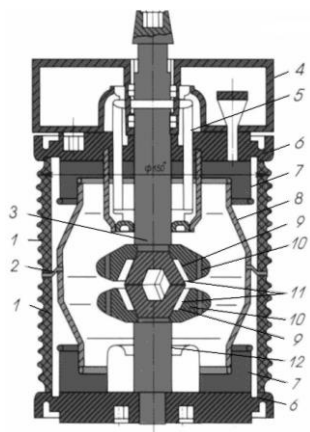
Камера вакуумная КДВ-10: 1 - керамический изолятор; 2 - кольцевая металлическая прокладка; 3 - подвижный контактный стержень; 4 - направляющая; 5 - сильфон; 6 - фланец; 7 - потенциальный экран; 8 - беспотенциальный экран; 9 - зазор; 10 - дугогасительный электрод; 11 - контакты; 12 - неподвижный контактный стержень
